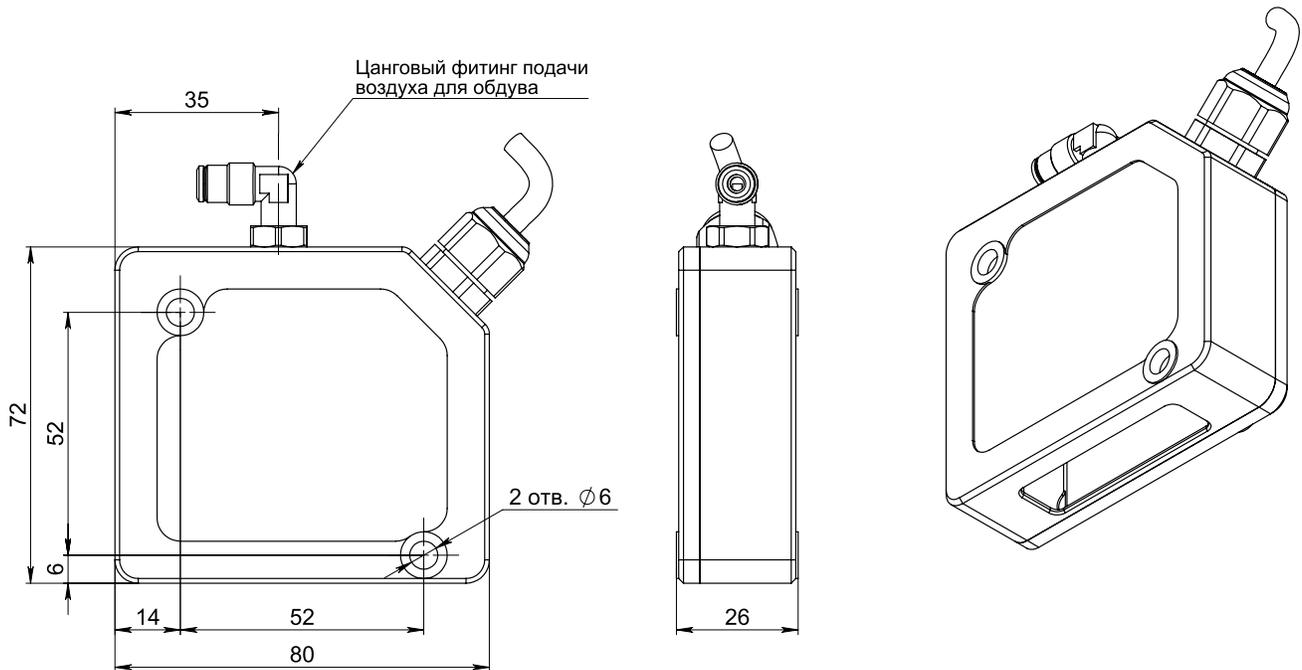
Охлаждающий кожух для корпуса типа A
